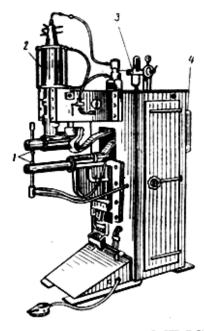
Машина точечной сварки МТ-IC10: 1 — электроды, 2 — пневмоцилиндр, 3 — лубрикатор, 4 — регулятор времени
